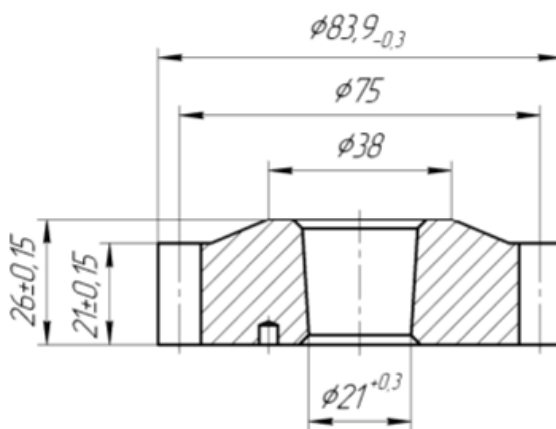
Заготовка, полученная методом торцевой штамповки
